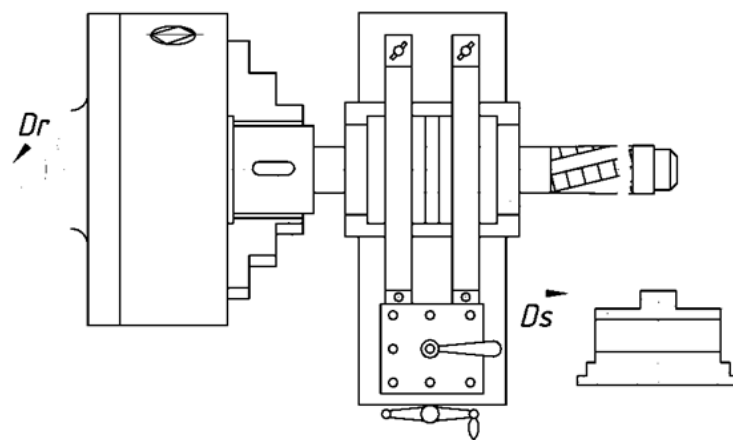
Загальний вигляд встановлення інструменту
